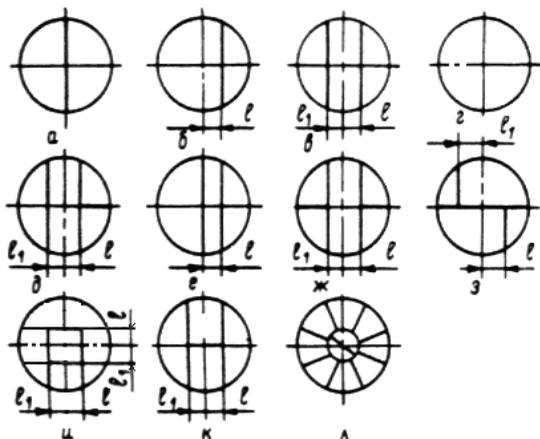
Допустимое расположение сварных швов на заготовке днища
